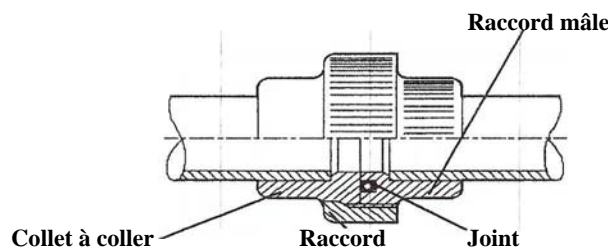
Assemblage par manchon à bague d'étanchéité
